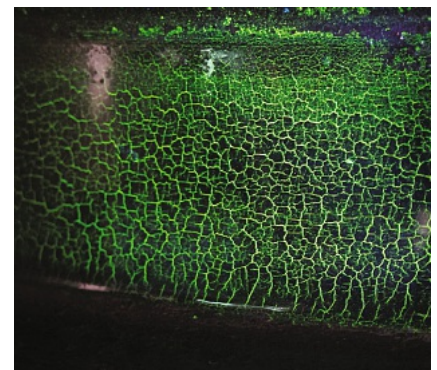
Temperaturwechsellisse auf der formgebenden Oberfläche einer Druckgießform, sichtbar gemacht mittels Magnetpulverprüfung unter UV-Licht.
